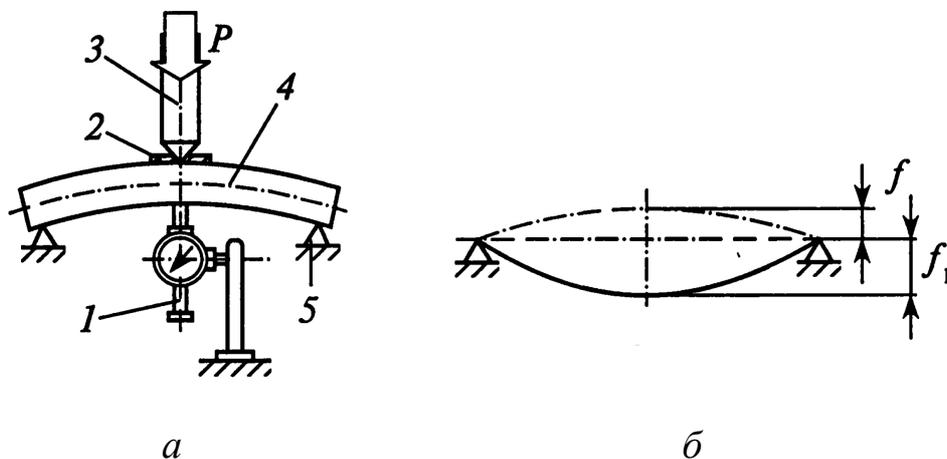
Схемы холодной правки вала: а – монтажная; б – расчетная: 1 – индикатор; 2 – прокладка; 3 – нажимной шток; 4 – вал; 5 – опоры
